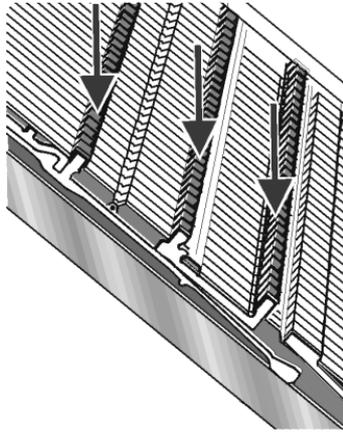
Engrase de los talones de la pieza de acoplamiento y del tornillo cilíndrico
